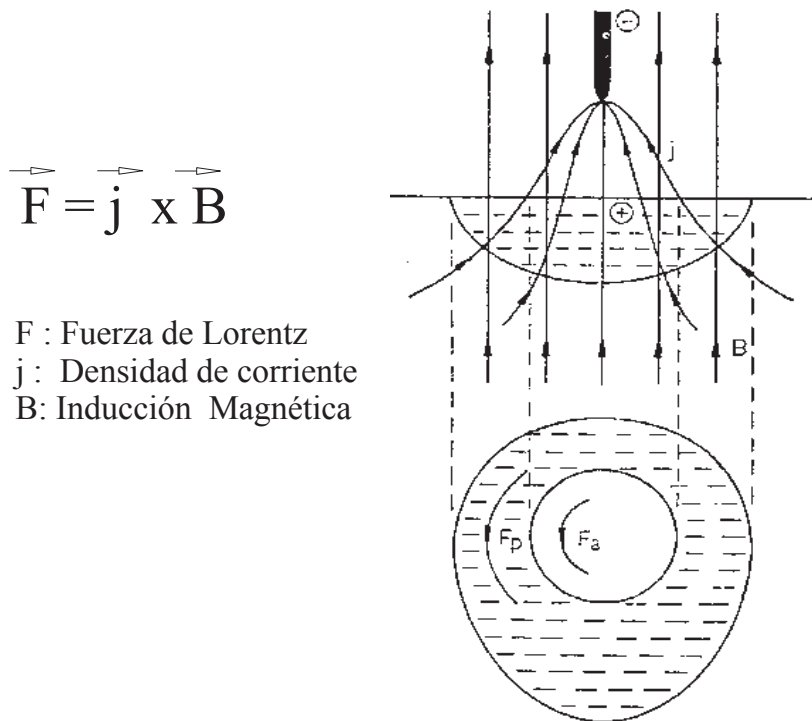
Representación esquemática de la influencia de un campo magnético externo en la piletta de soldadura. j: densidad de corriente B: inducción magnética Fa: fuerza de acción en el arco Fp: fuerza actuando en la piletta de soldadura [6].
